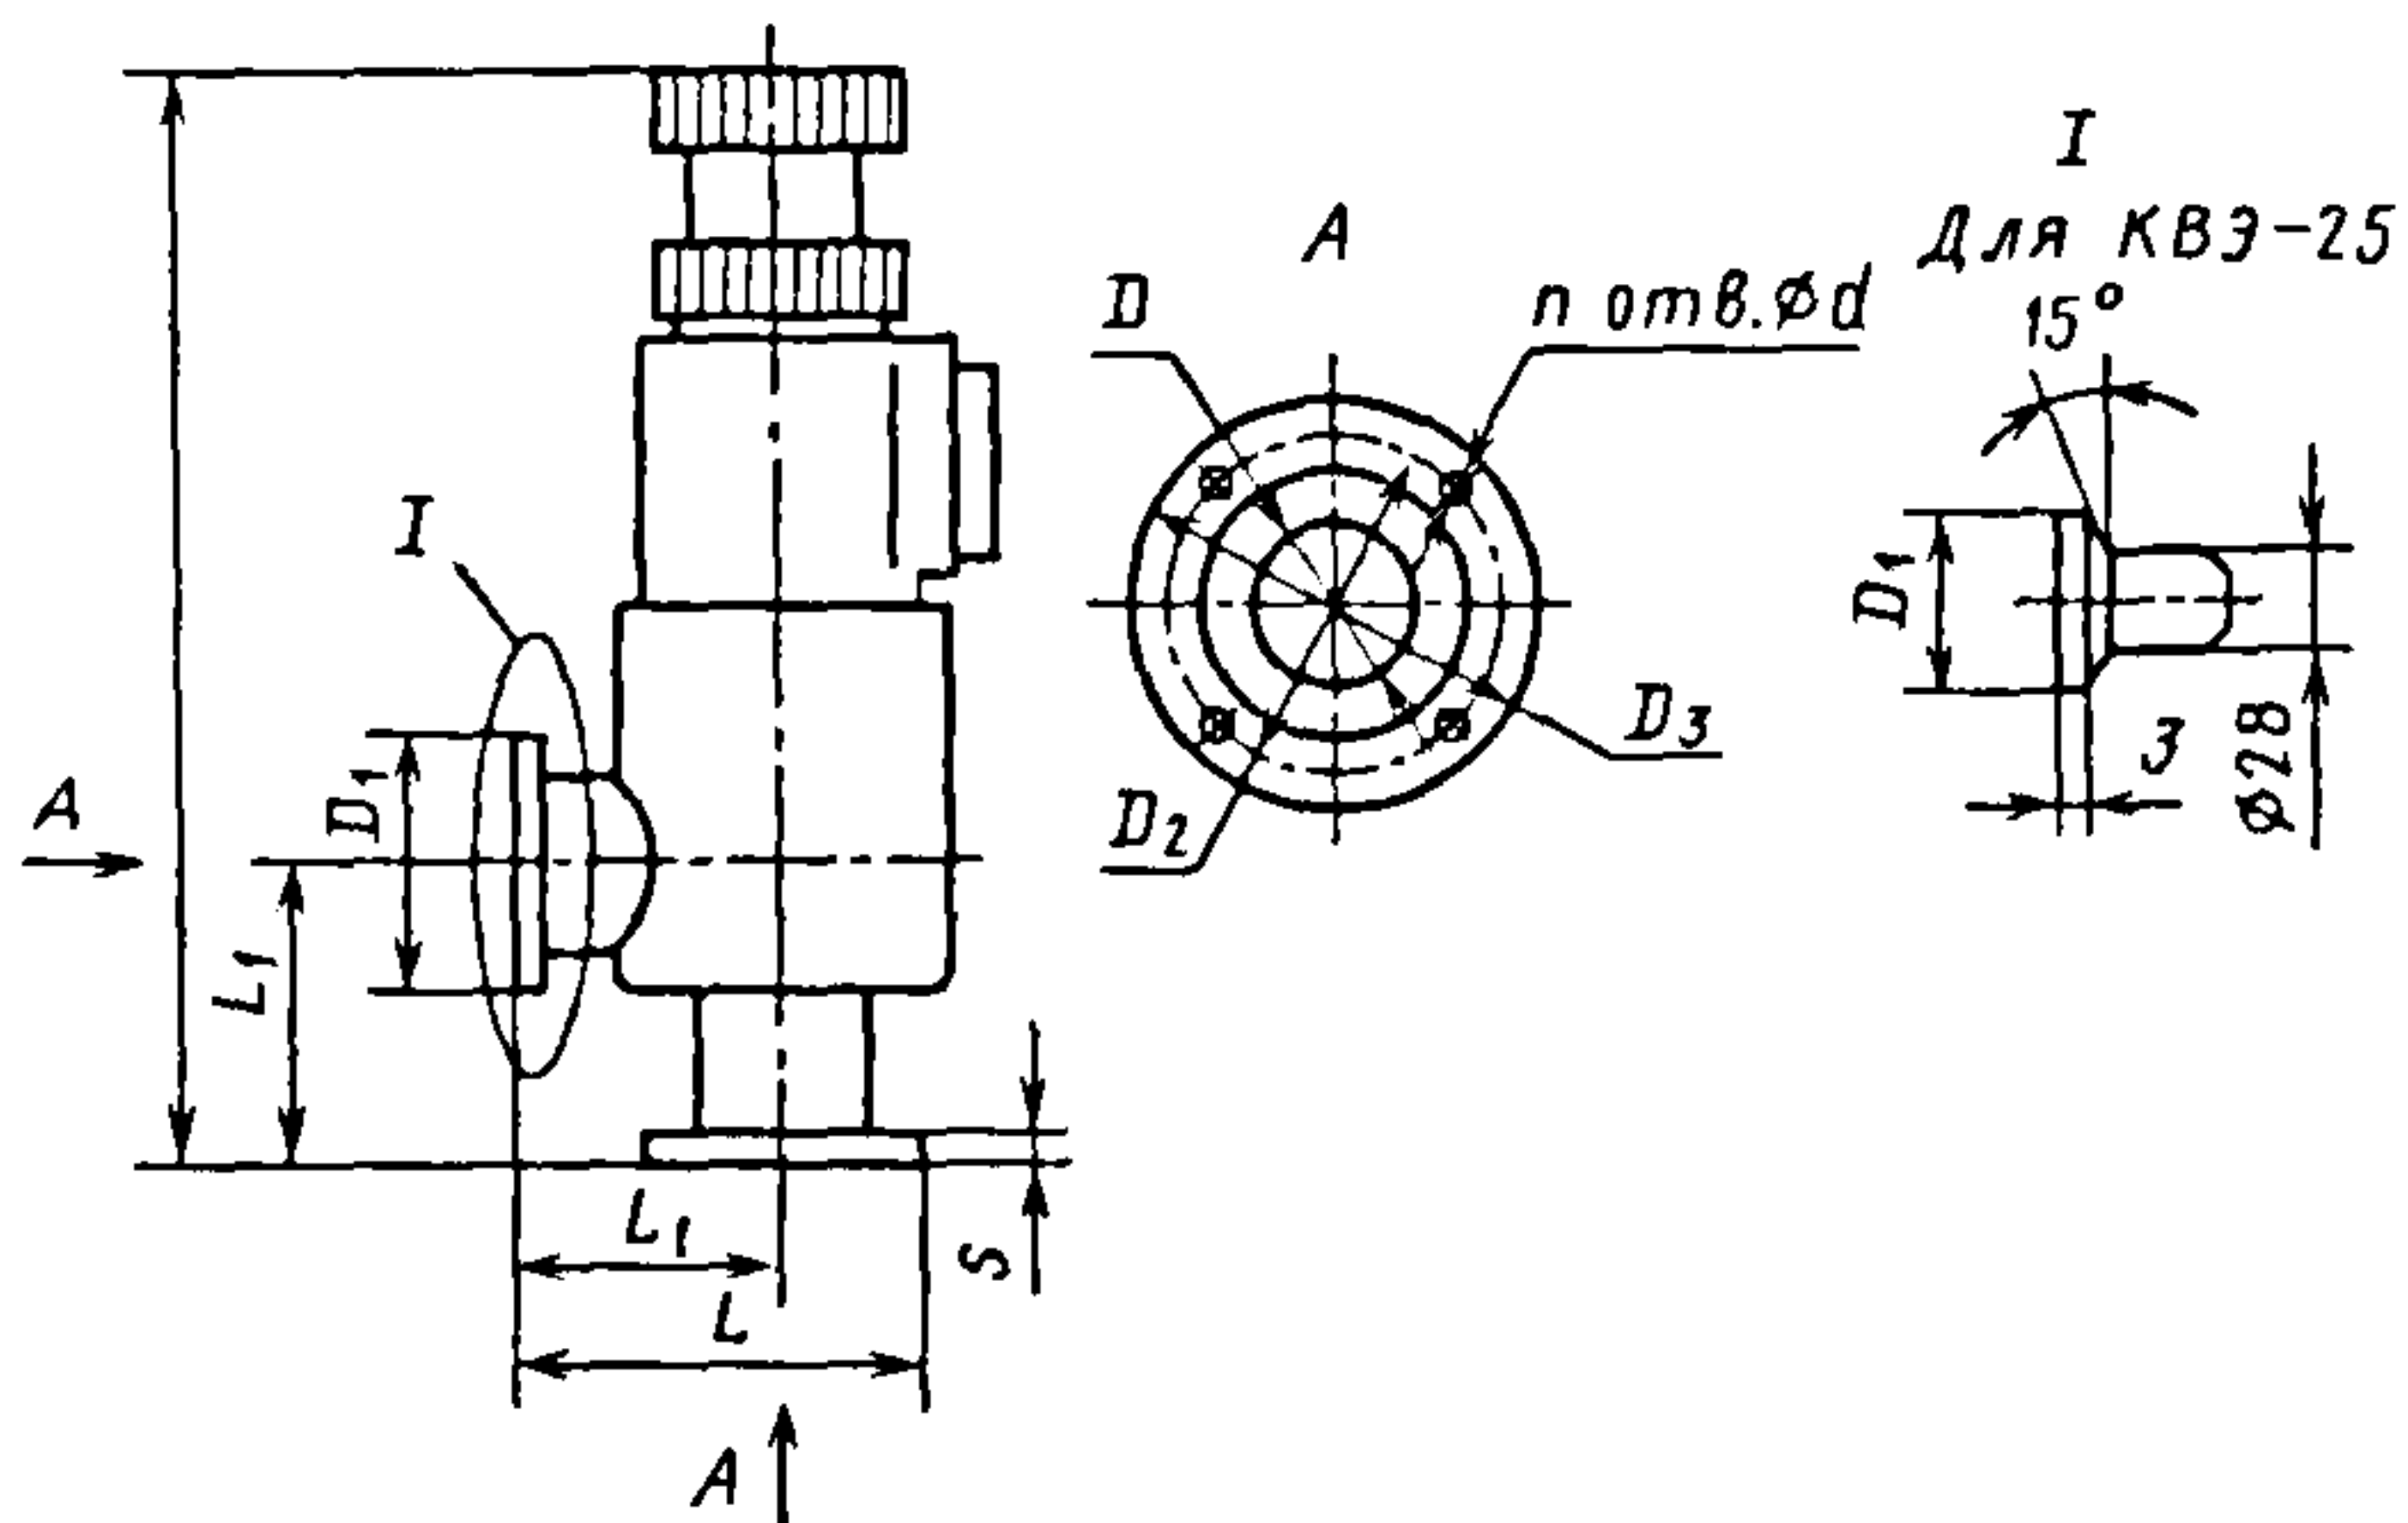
Габаритный чертеж клапана типа КВЭ
